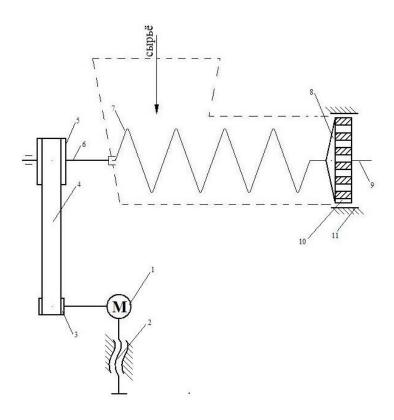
Кинематическая схема привода мясорубки с одним шнеком, расположенным горизонтально: 1 — электромотор; 2 — подмоторная плита; 3 — шкив; 4 — клиновый ремень; 5 — ведущий шкив; 6 — вал; 7 — измельчительный шнек; 8 — нож; 9 — палец шнека; 10 — центральное отверстие решетки; 11 — корпус шнека; 12 — винт; 13 — гайка
